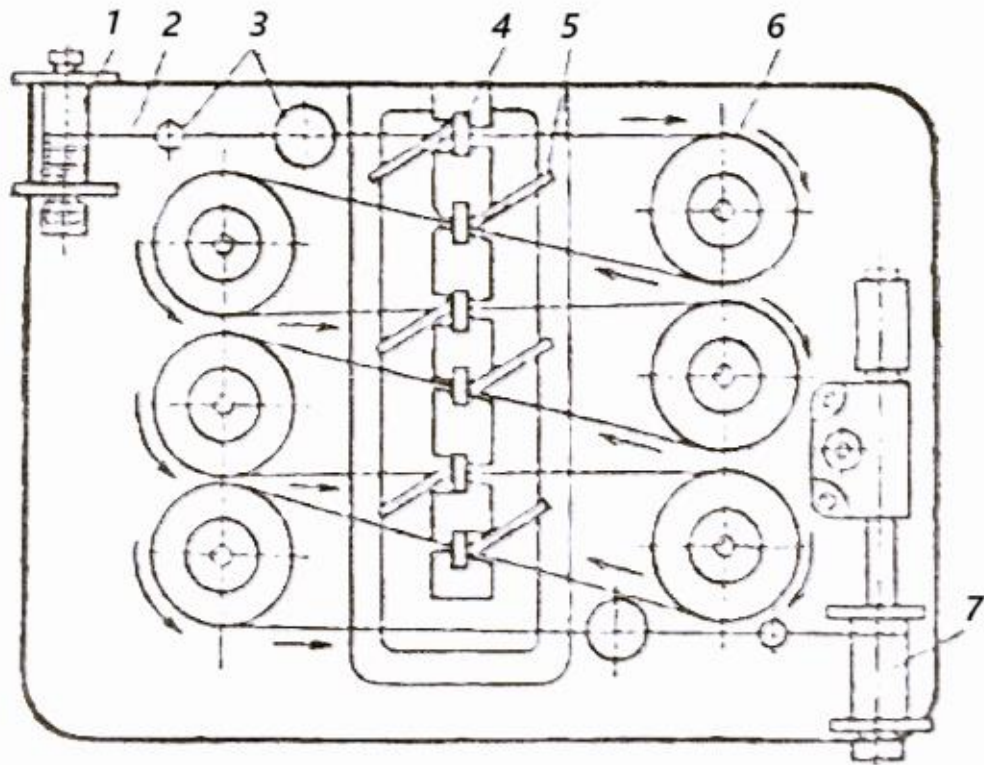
Схема розташування багаторазового волочильного стану:
